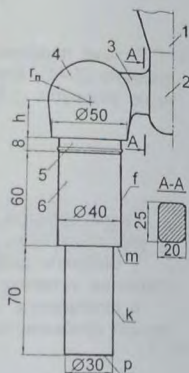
Схема модельного блока отливки "Цилиндр"
